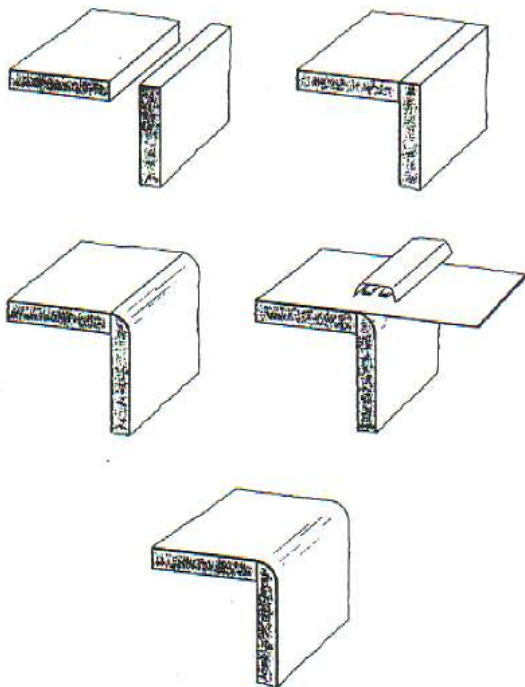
Kompaktträgerplatte aus vorgefrästen Teilen
